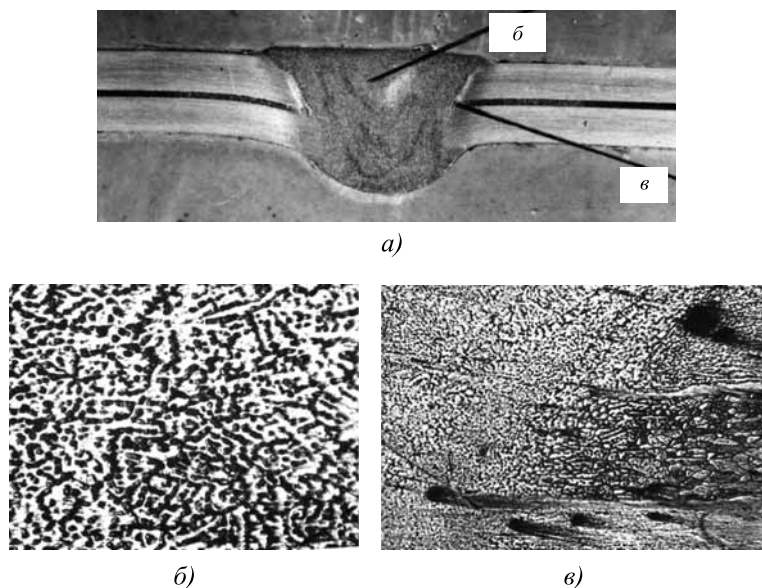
Макроструктура сварного соединения, выполненного автоматической аргодуговой сваркой (а), микроstructures шва (б) и зоны сплавления (в): а — $\times 3$; б, в — $\times 430$
